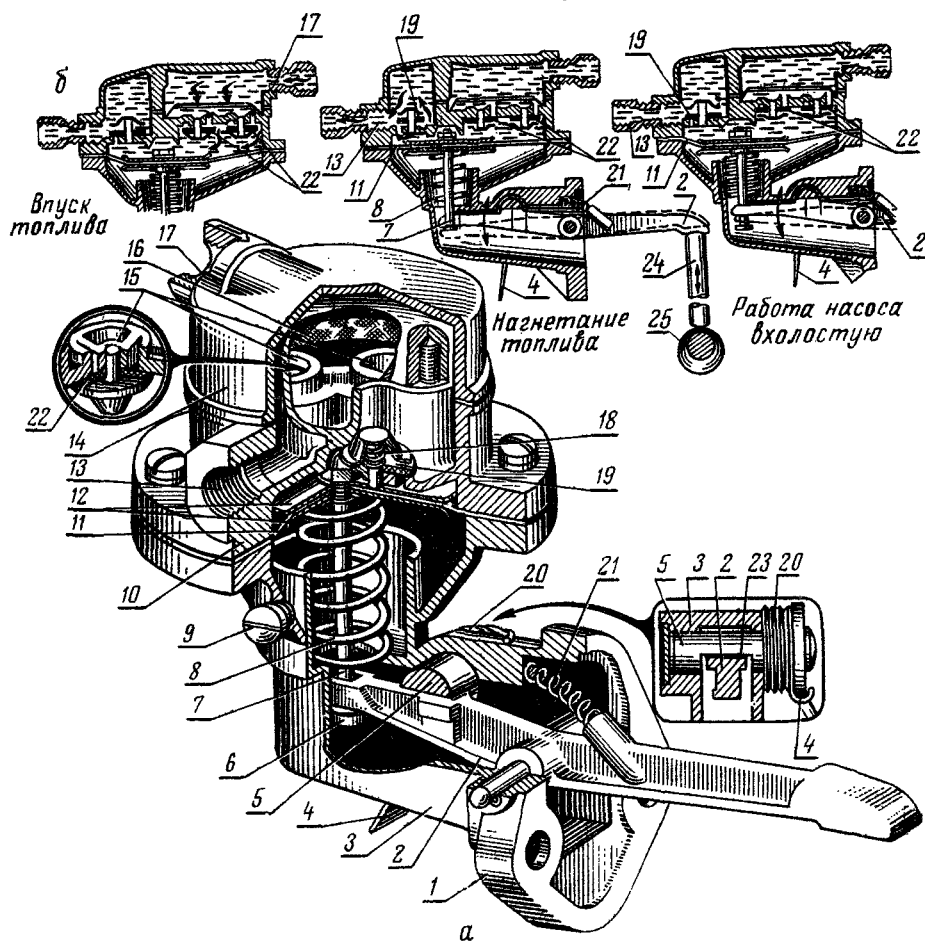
Топливный насос диафрагменного типа Б-9 двигателя ЗИЛ-130:
